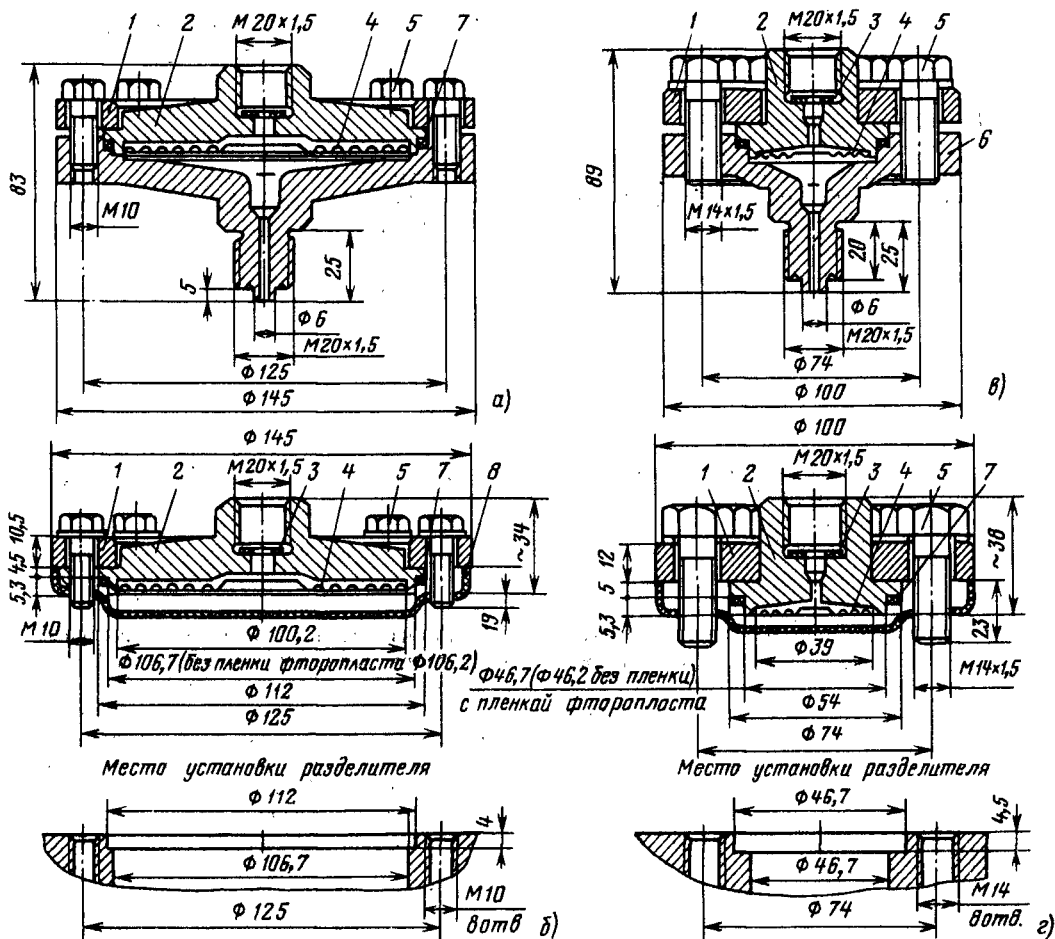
Габаритные, установочные и присоединительные размеры мембранных разделителей РМ:
